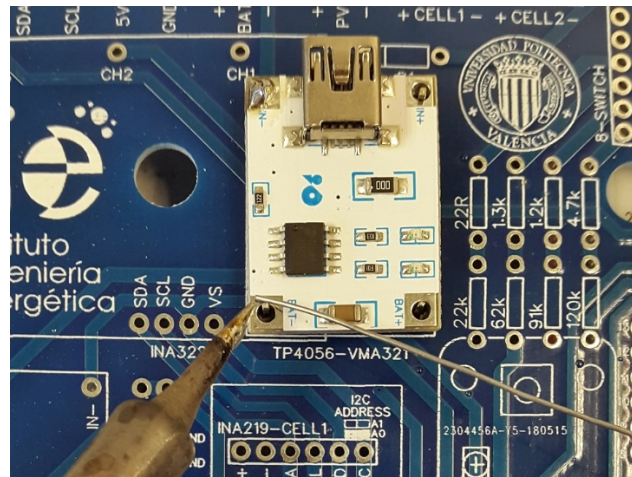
Soldadura de los componentes directamente en la placa.
